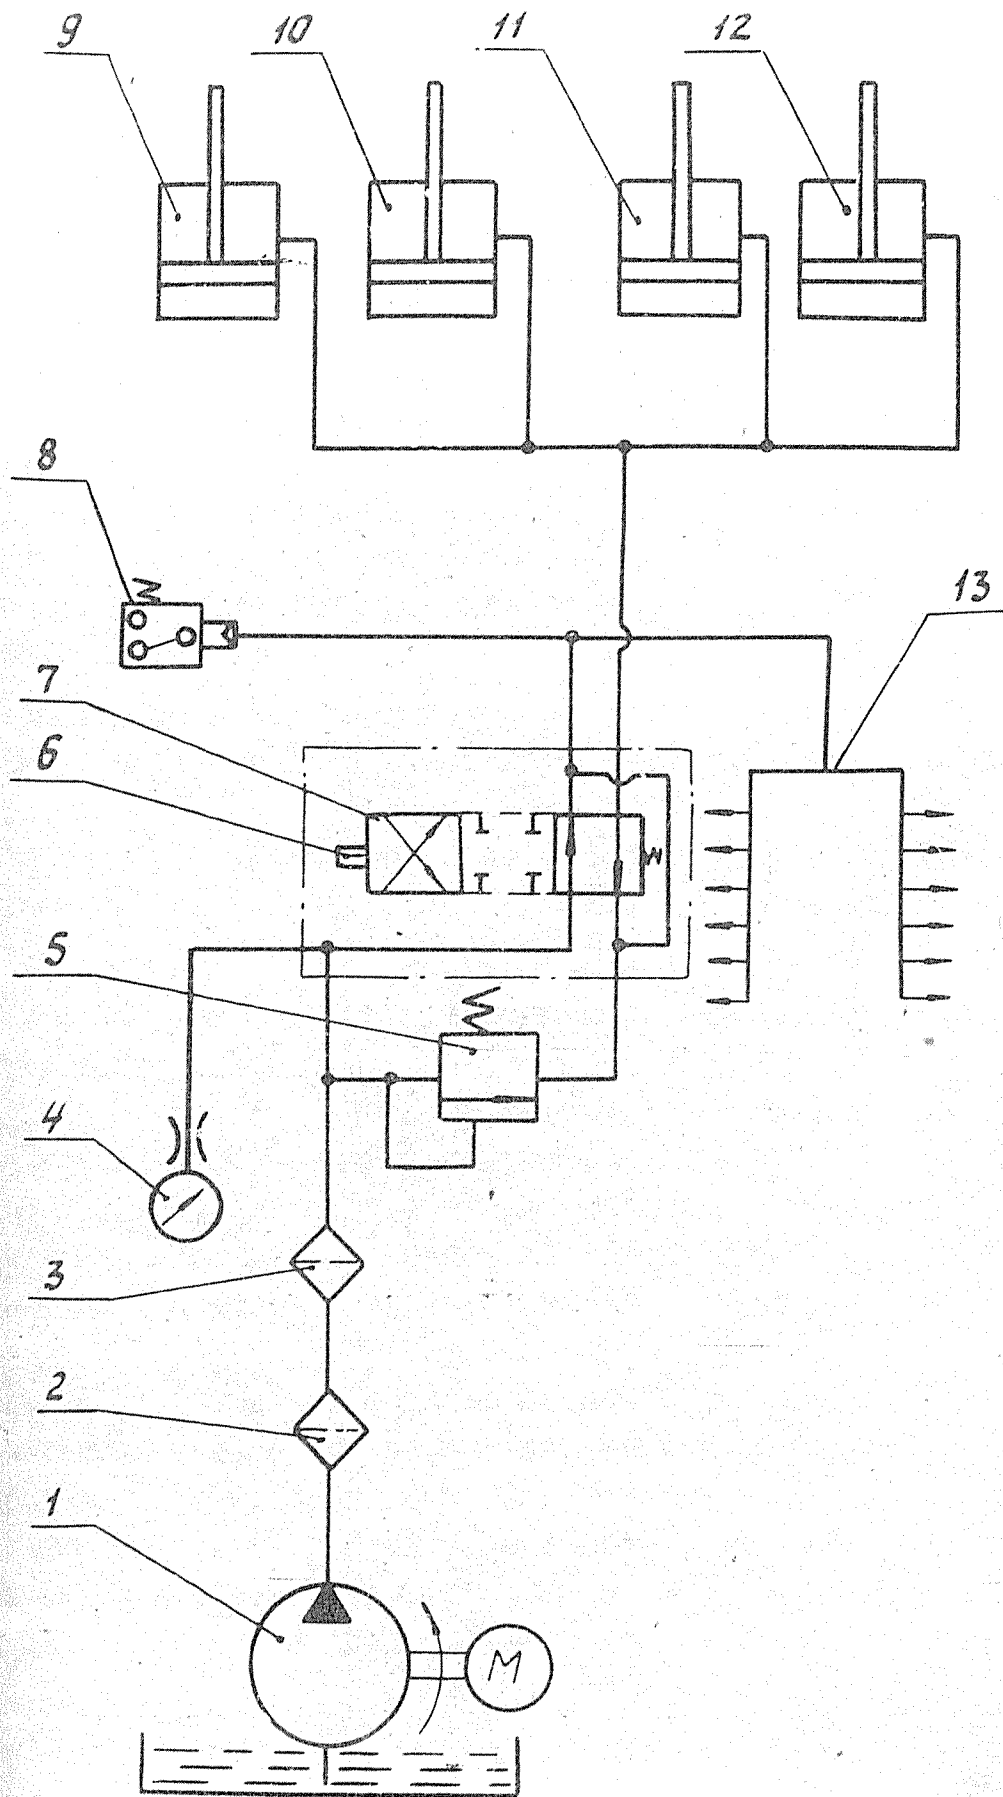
Гидросхема смазки редуктора и разжима прихватов полеречины.
